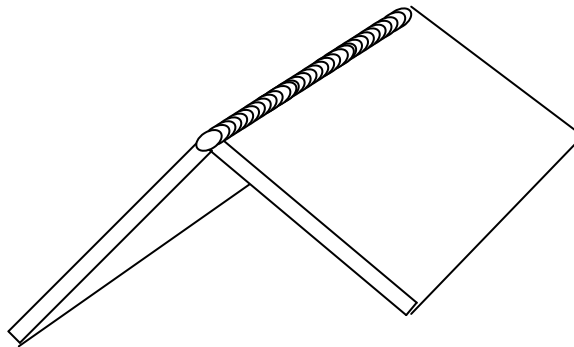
Soldadura en esquina en posición plana.
